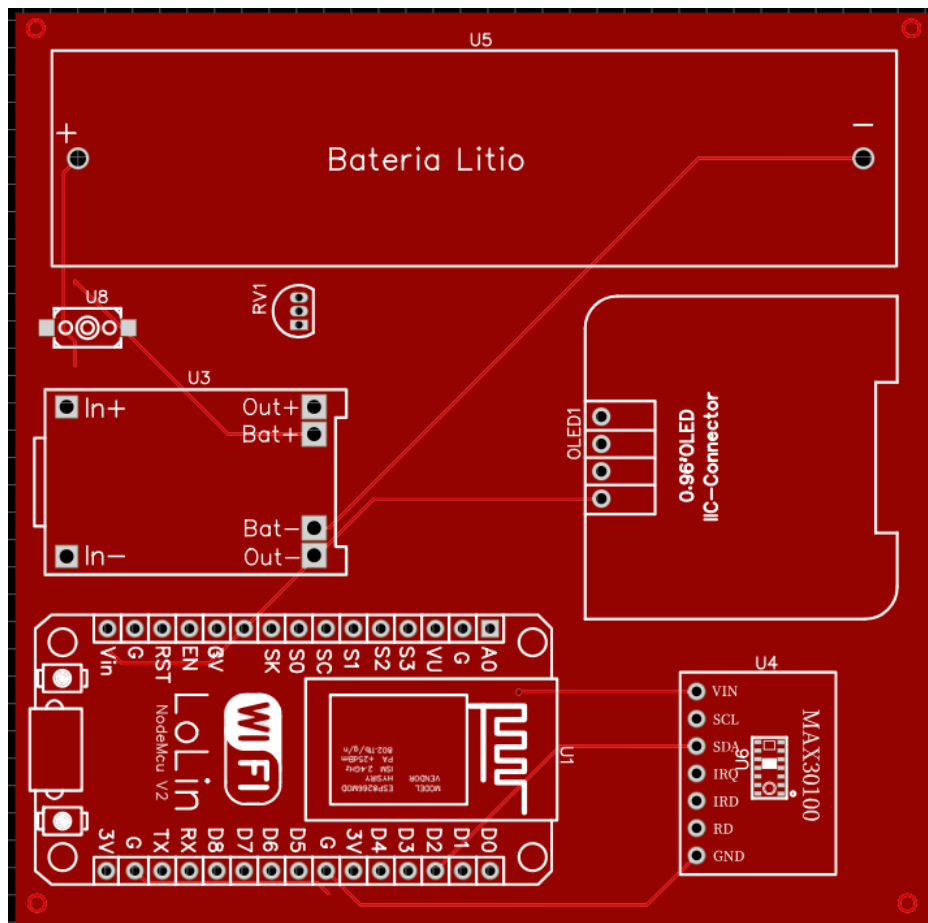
Tarjeta PCB del sistema de monitoreo IoT con vista frontal modelado en 2D.
